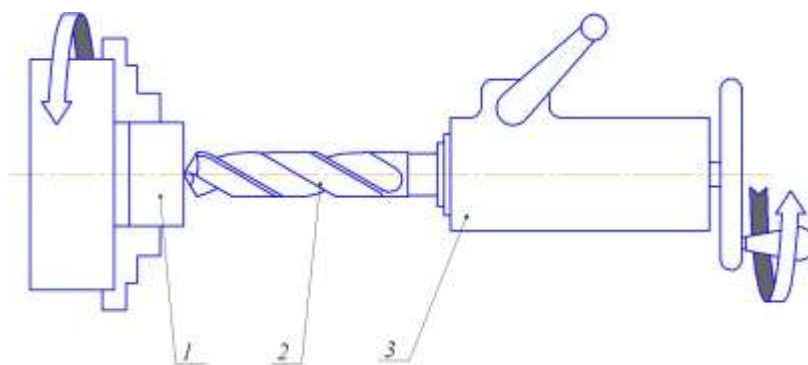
Сверление : 1- заготовка; 2- сверло; 3- задняя бабка
